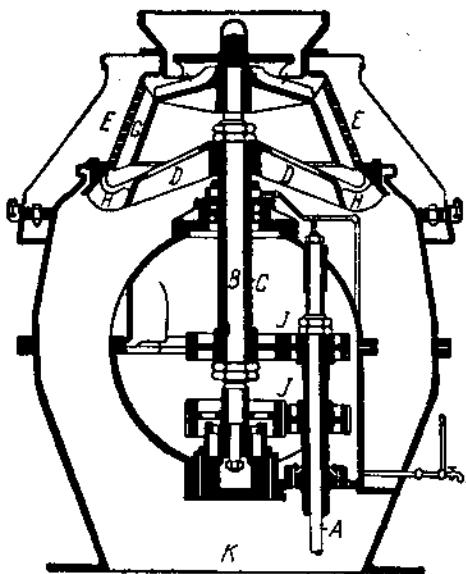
Вертикальная центрифуга непрерывного действия системы Эльмора. *A* — приводной вал, *B* — внутренний вал, *C* — наружный вал, *D* — стойка, *E* — вращающийся барабан, *F* — опора скребка.
